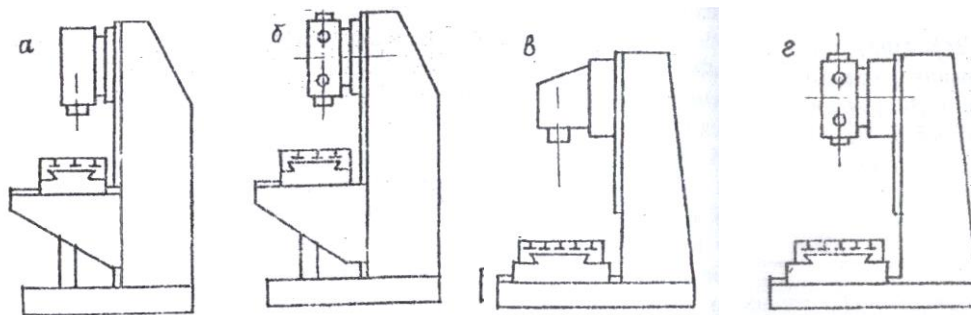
Виконання фрезерних верстатів з ЧПУ
